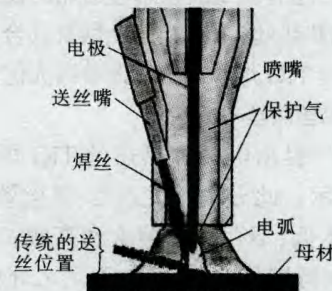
TOP-TIG 焊的原理示意图^[22]
